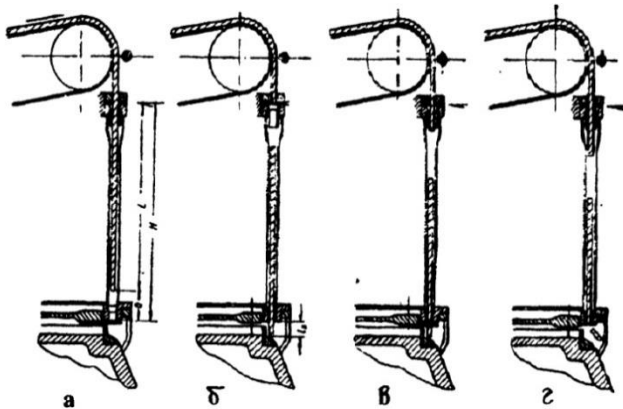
Схема різання порохового шнура на різальному агрегаті
